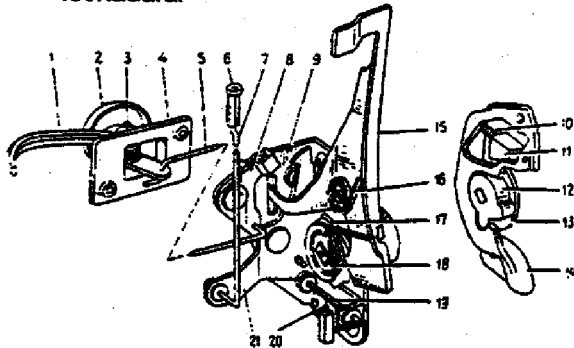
Conjunto da fechadura da porta dianteira: 1 - maçaneta interna; 2 - moldura de acabamento; 3 - pino de articulação; 4 - suporte da maçaneta interna; 5 - haste da maçaneta interna; 6 - botão da trava interna; 7 - haste da trava interna; 8 - alavanca de acionamento interno da fechadura; 9 - carcaça da fechadura; 10 - mola do trinco; 11 - trinco; 12 - rotor; 13 - apoio central; 14 - corpo do trinco; 15 - alavanca de acionamento externa; 16 - mola da alavanca de acionamento externa; 17 - trava; 18 - mola da trava; 19 - eixo de desconexão da fechadura; 20 - haste de desconexão da fechadura; 21 - alavanca da trava da fechadura.
